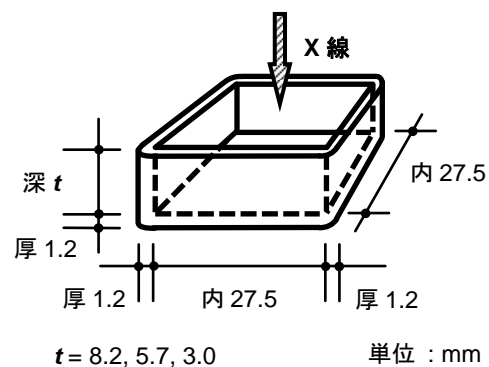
試料容器の形状および寸法。 Figure and dimension of specimen container.
